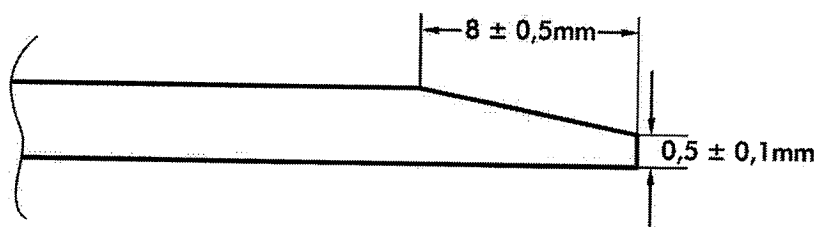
Dimensões do chanfro desquinado tipo sobreposto
